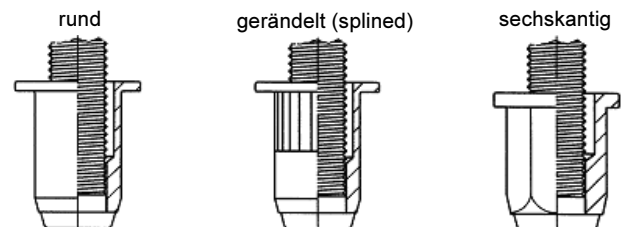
Hülseausführungen von Blindnietgewindebolzen.
